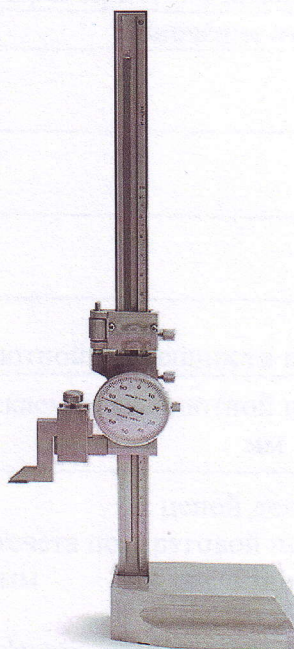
Общий вид штангенрейсмаса ШРК
